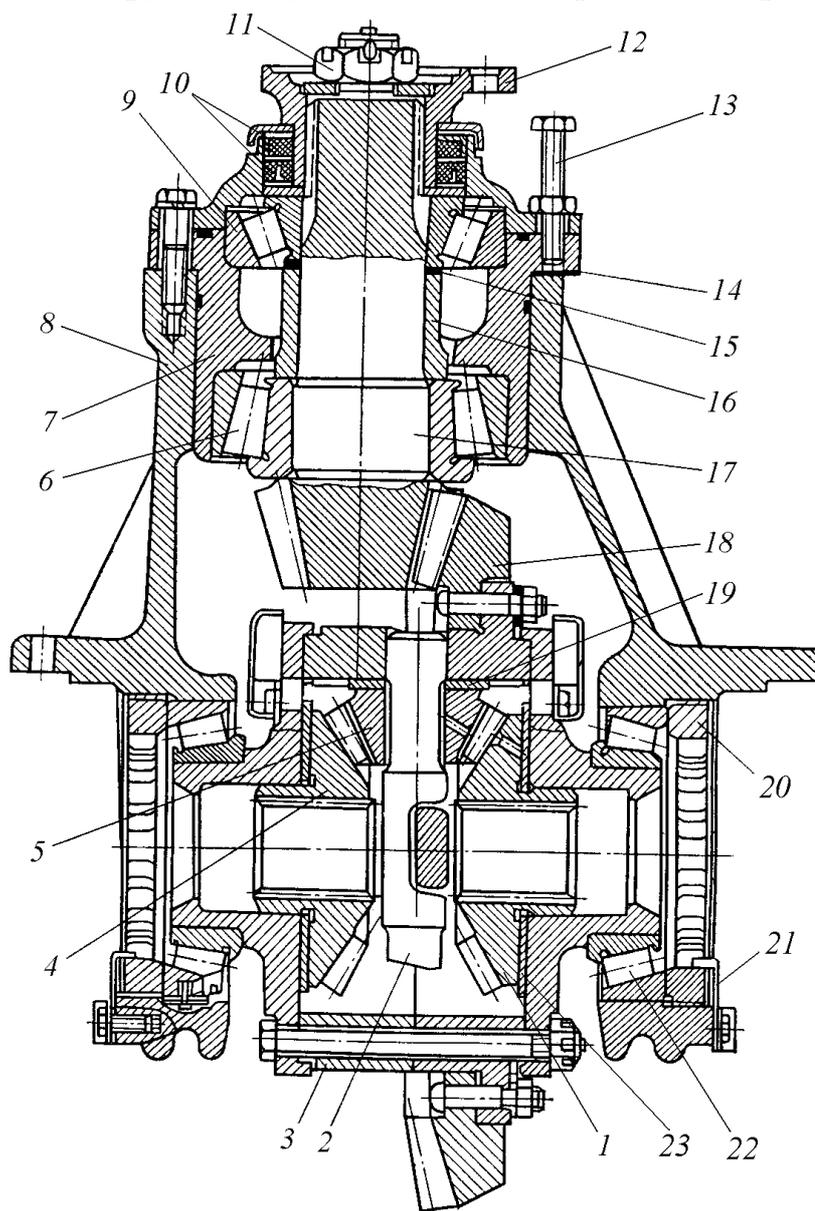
Редуктор ведущего моста трактора Т-150К: 1, 4 - полуосевые шестерни; 2 - ось сателлитов; 3 - корпус дифференциала; 5 - сателлит; 6, 9 и 22 - конические роликовые радиально-упорные подшипники; 7 - стакан; 8 - корпус редуктора; 10 - манжетные уплотнения; 11 - гайка; 12 - фланец; 13 - болт; 14, 15 - регулировочные прокладки; 16 - распорная втулка; 17 - вал - шестерня центральной передачи; 18 - колесо центральной передачи; 19 - опорная шайба сателлита; 20 - регулировочная гайка; 21 - пластина стопорная; 23 - опорная шайба полуосевой шестерни
